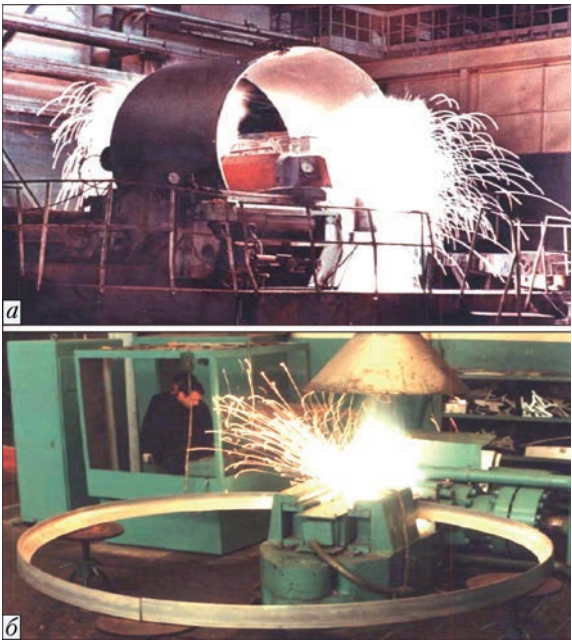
Приклади використання контактно-стикового зварювання у виробництві фрагментів конструкцій аерокосмічної техніки з високоміцного сплаву АМгб: а – зварювання обичайки корпусу паливного баку; б – зварювання шпангоутів
